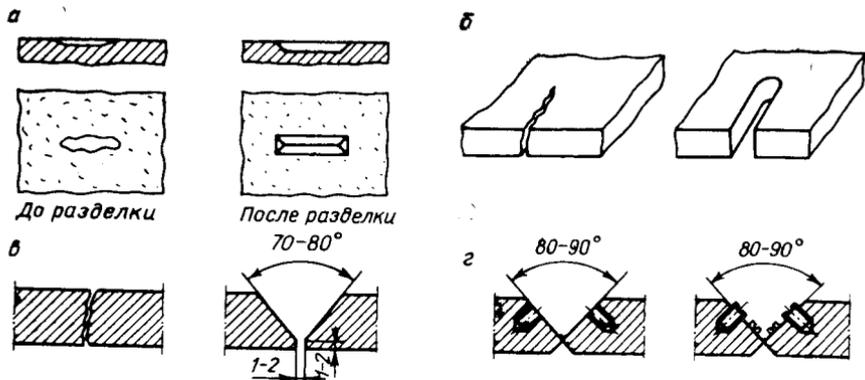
Подготовка дефекта к сварке:
